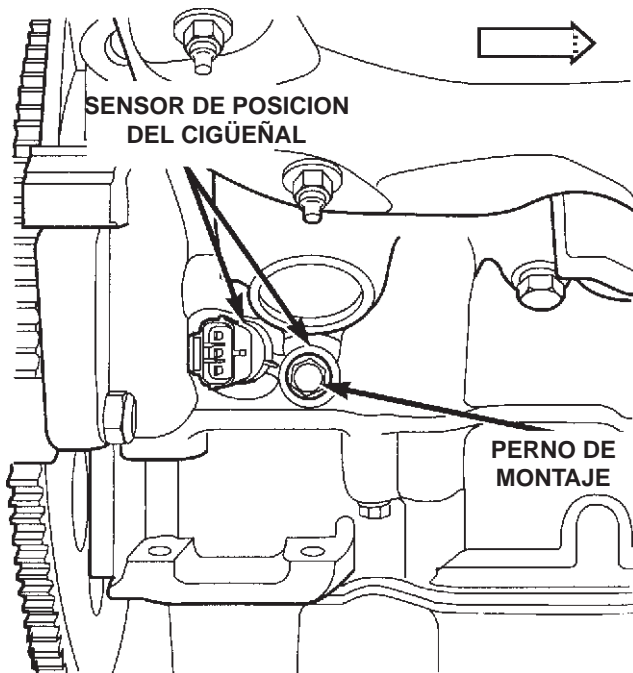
Montaje y desmontaje del sensor CKP del motor V-8 de 4.7 L
